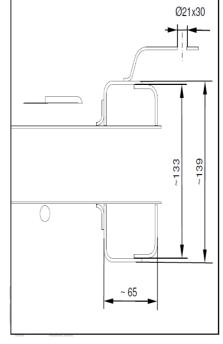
Sezione R-R (Amarok SC/DC)
